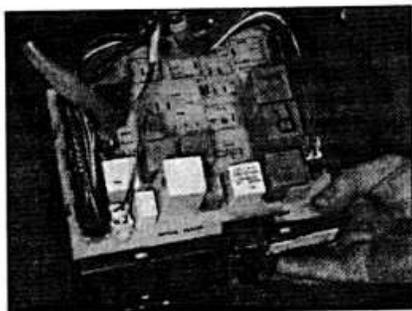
Расположение реле с обратной стороны щитка с плавкими предохранителями.
